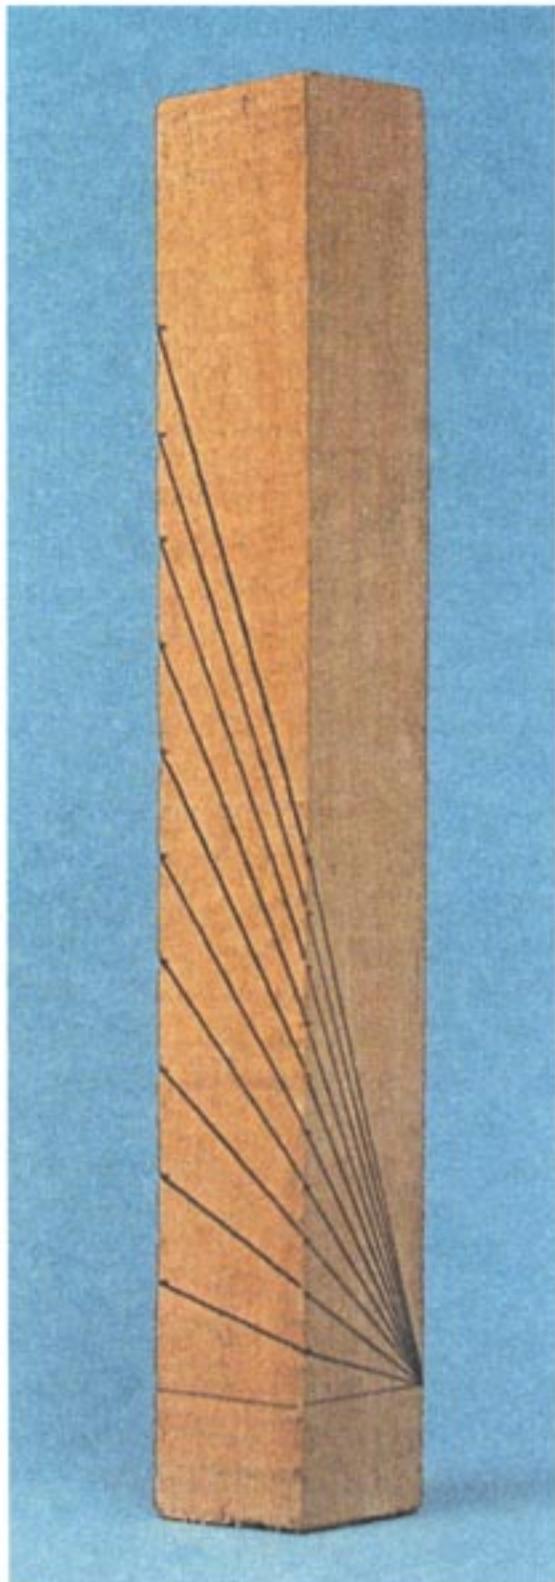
На данной заготовке видно, как от увеличения шага линия разметки выпрямляется по отношению к заготовке
